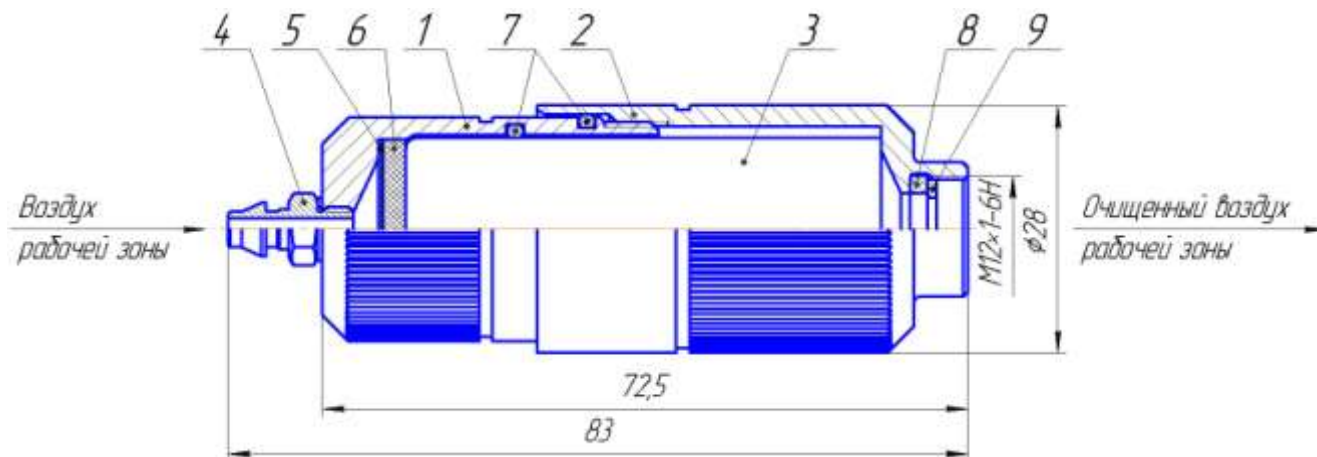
крышка; 2 – корпус; 3 - патрон с сорбентом; 4 – штуцер;
